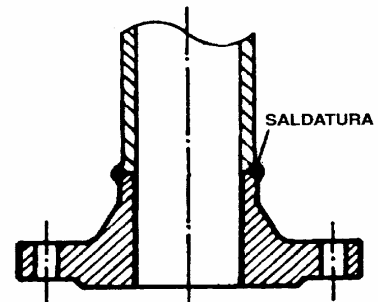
Modalità di giunzione mediante saldatura fra tubo e flangia a collare.
